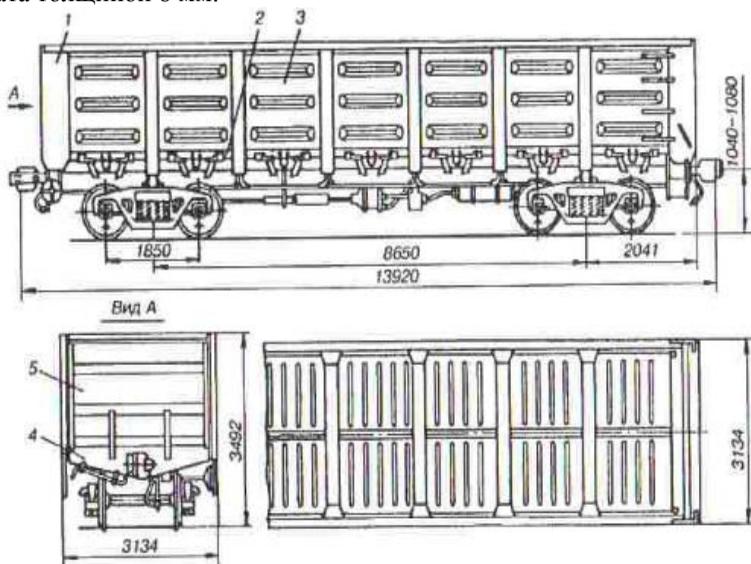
Универсальный 4-осный полувагон с глухими торцевыми стенами
